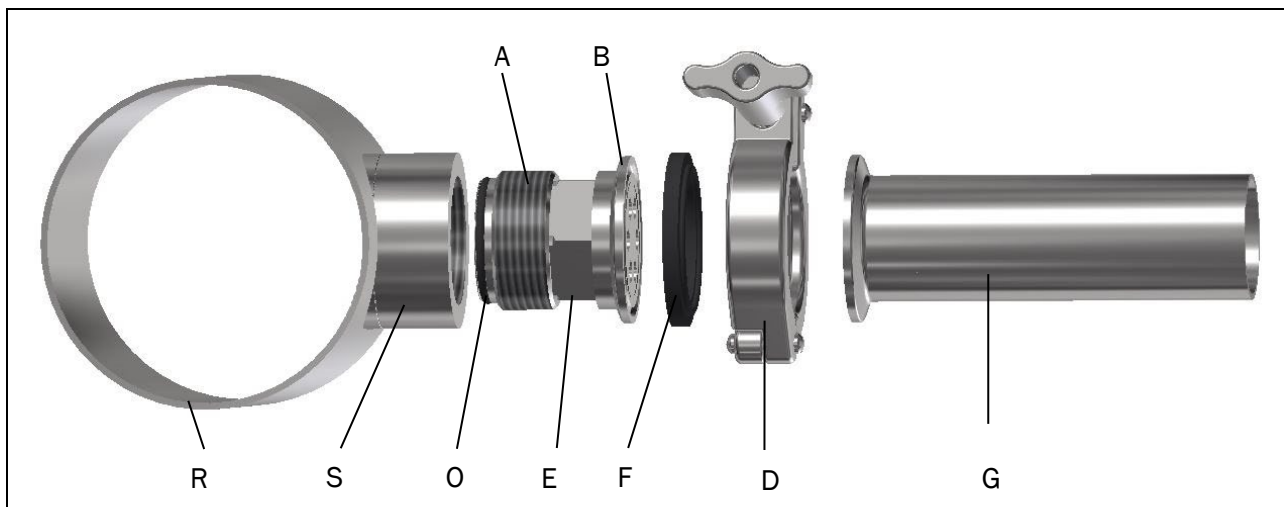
Einbau TANKO-RF mit PA Gewinde an Gewinde-Behälterstutzen
